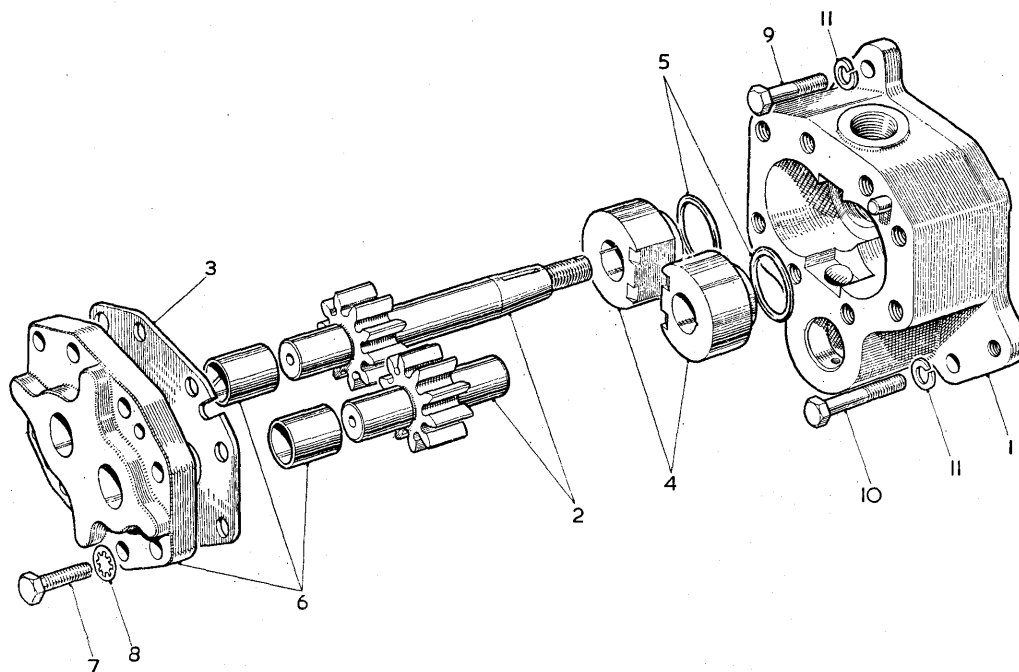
Komponenterne i hydraulisk pumpe af nyere type.
